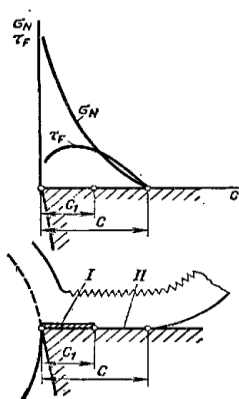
Два участка трения на передней поверхности токарного резца:
